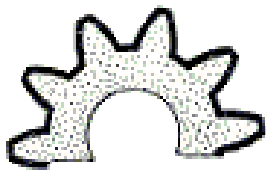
Поперечний переріз зубів шестерні, загартованих ТВЧ.
